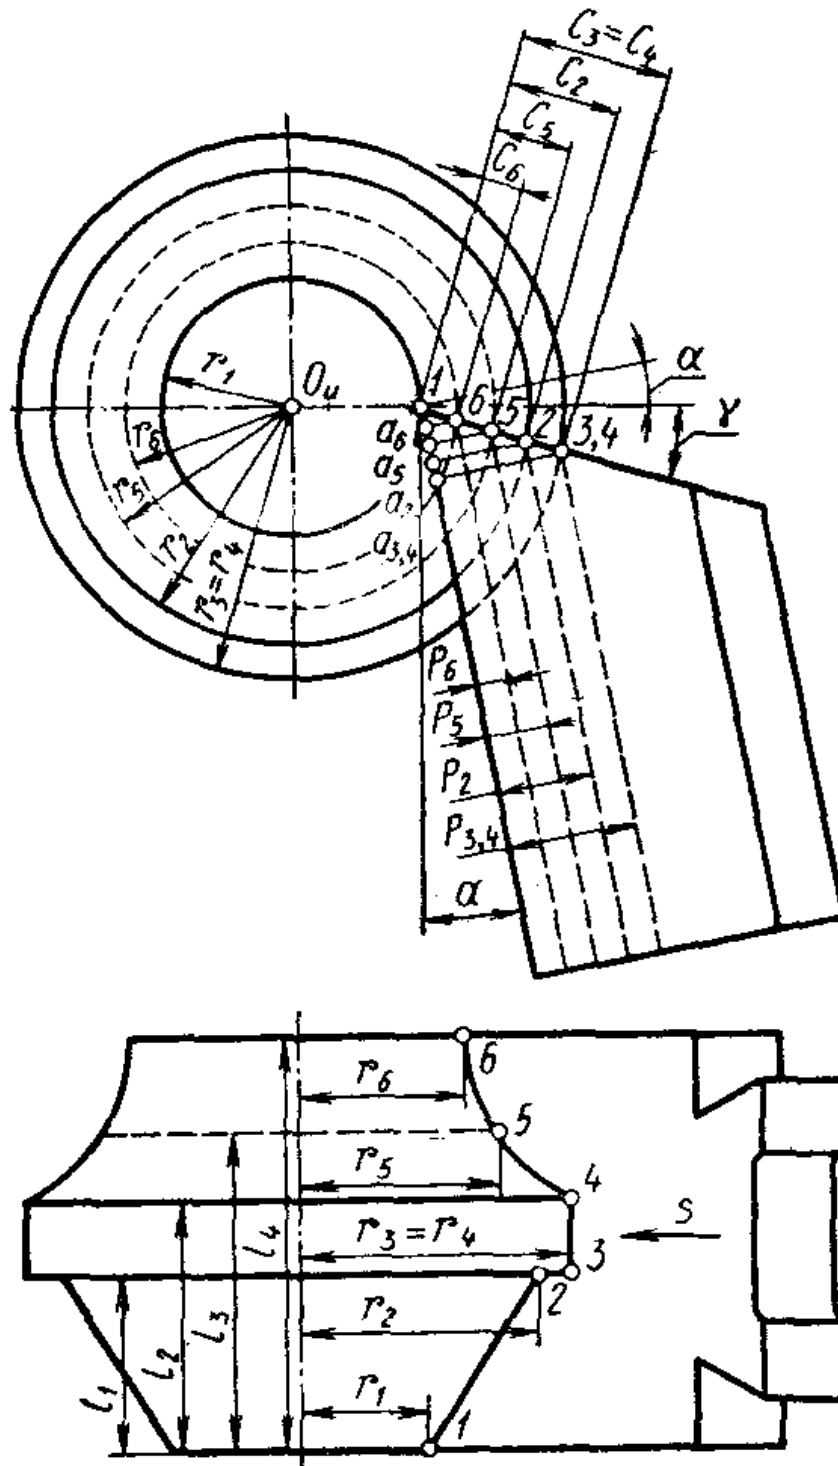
Схема для корекційного розрахунку призматичного фасонного різця, встановленого базовою точкою 1 по висоті лінії центру деталі
